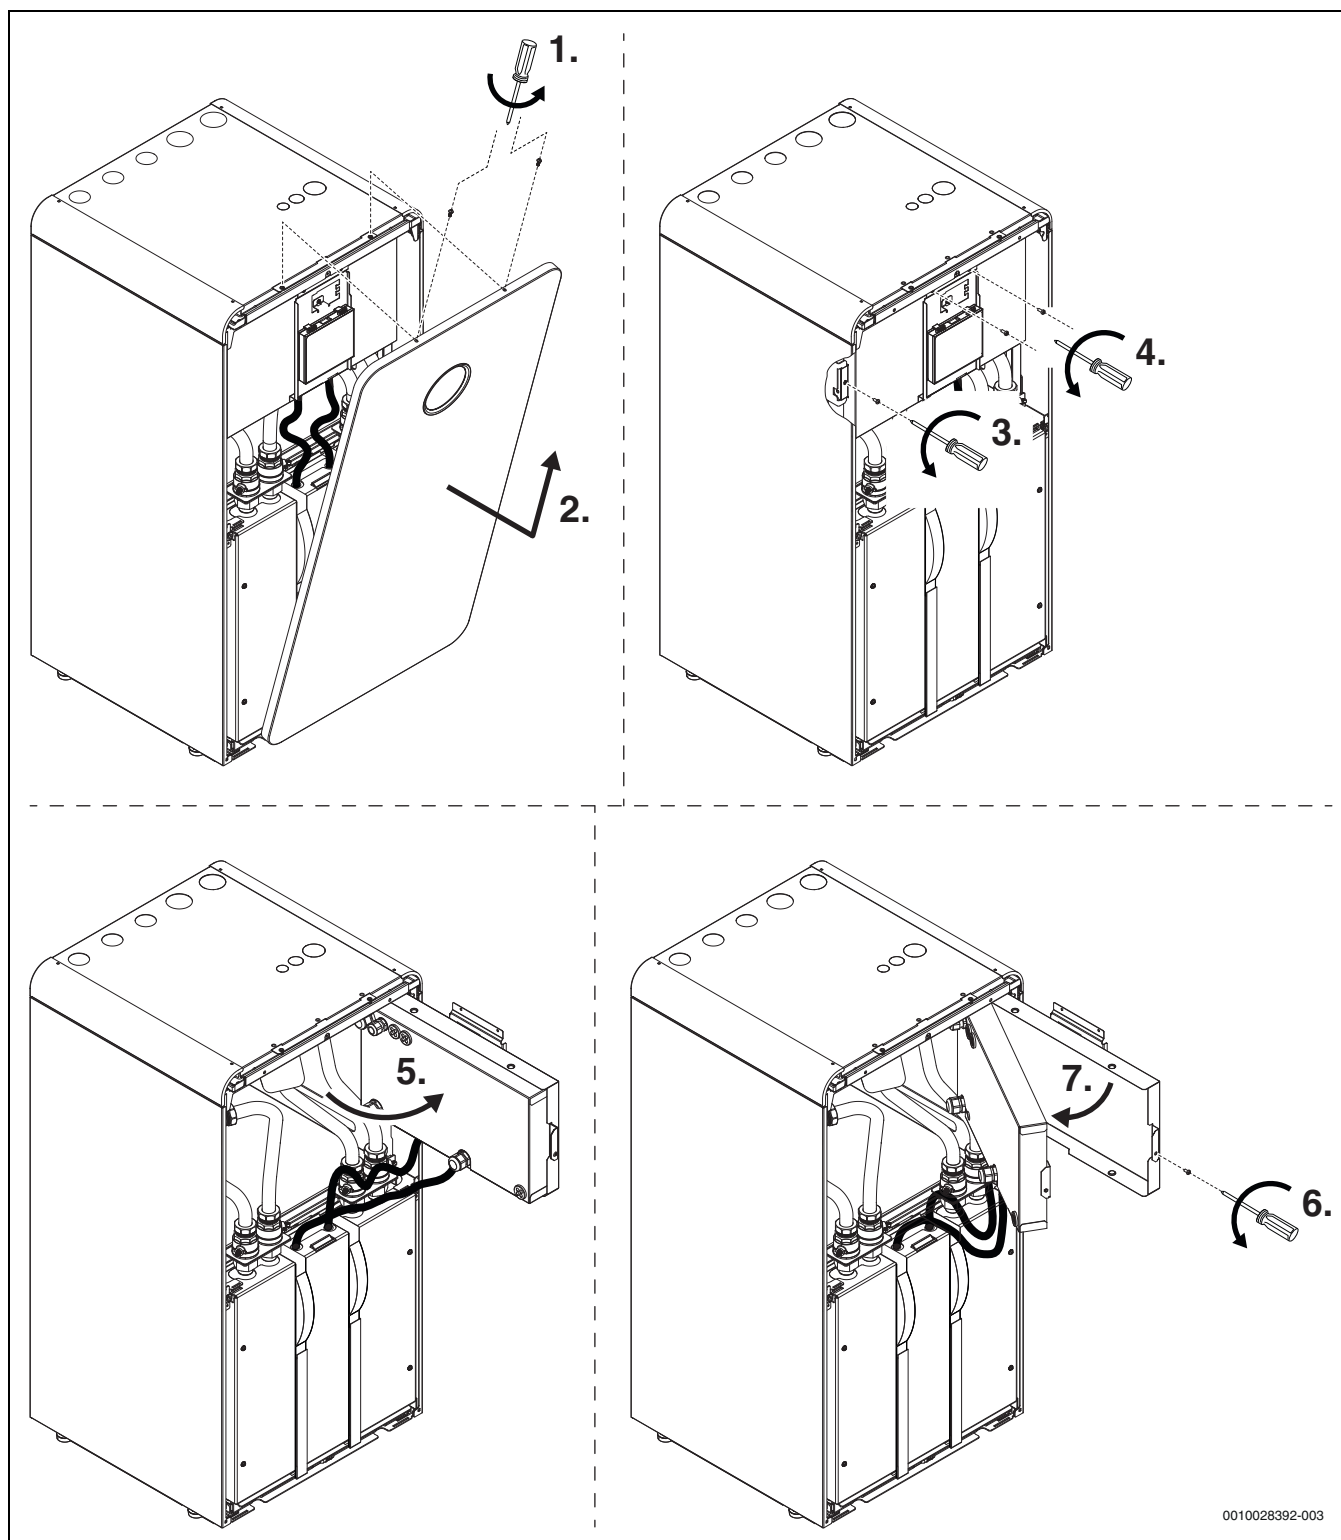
Adgang til hydraulikmodulet/klemmekassen
